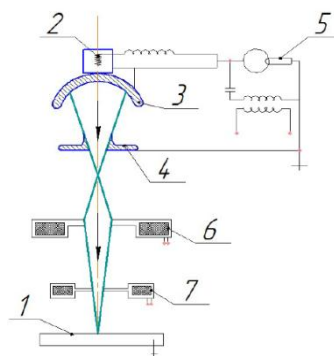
Схема процесса электронно-лучевой сварки
